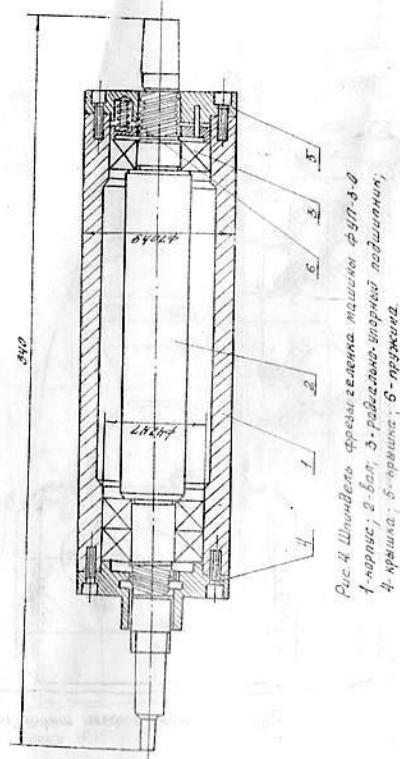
Шиндельный фрезер с лезвиями молдингов ФУП-3-0.
